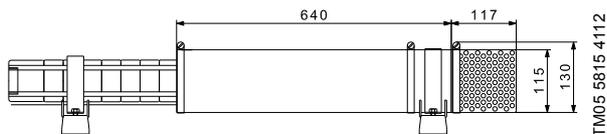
Kühlmantel und Einlaufsieb für die 4"-SQFlex
